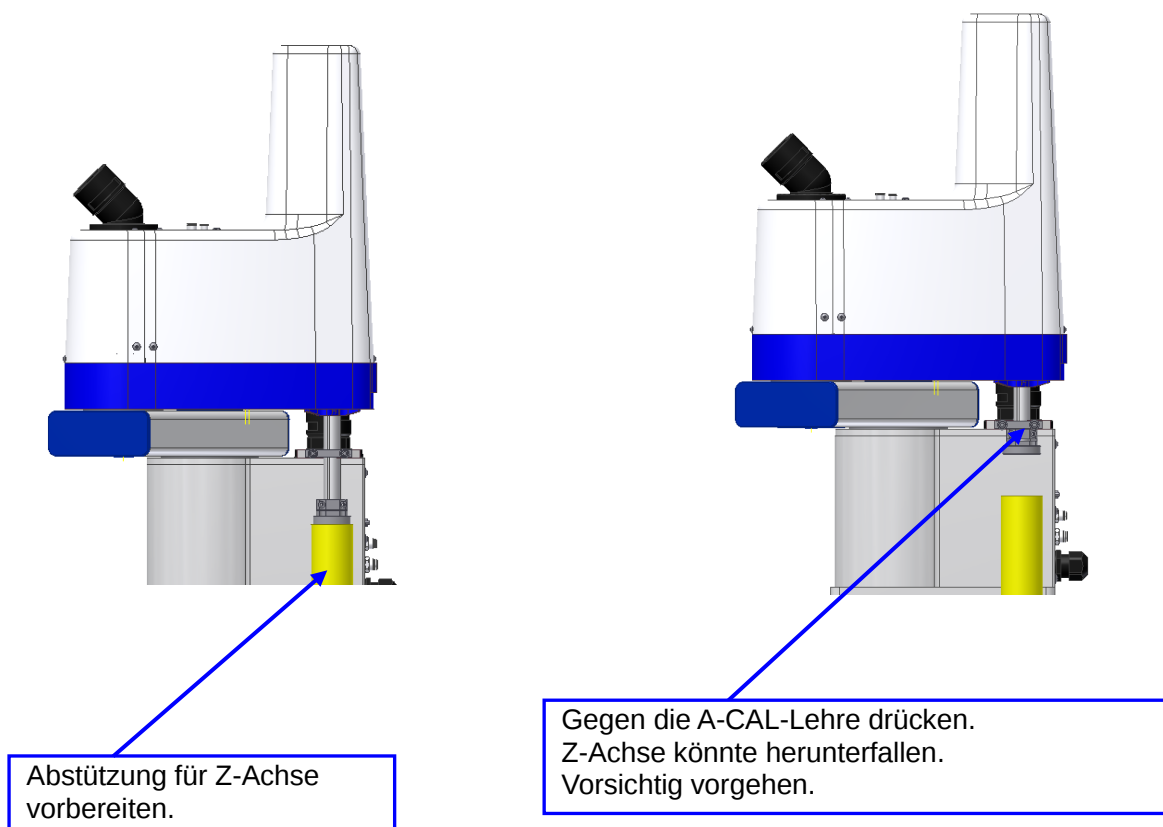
Z-Achse gegen die A-CAL-Lehre drücken
